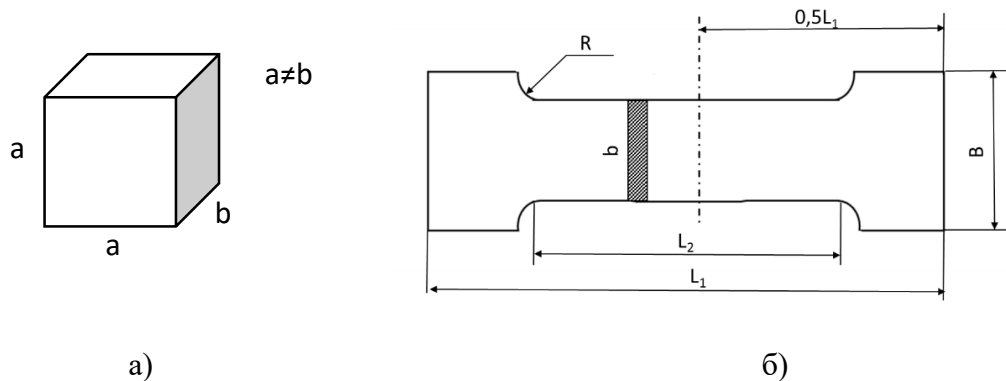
Образец для испытаний на сжатие (а) плоский образец для испытаний на растяжение (б)
